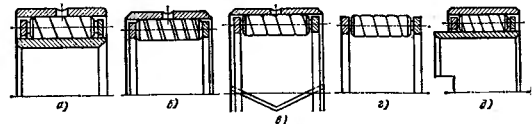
Роликоподшипники с витыми роликами типов: а — 5000; б — 35000; в — 45000; г — 65000; д — 15000
